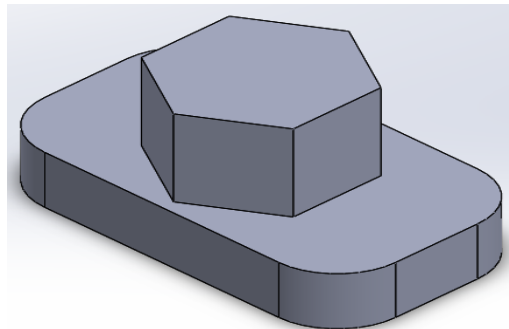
Pieza macho para pruebas de tolerancia.
